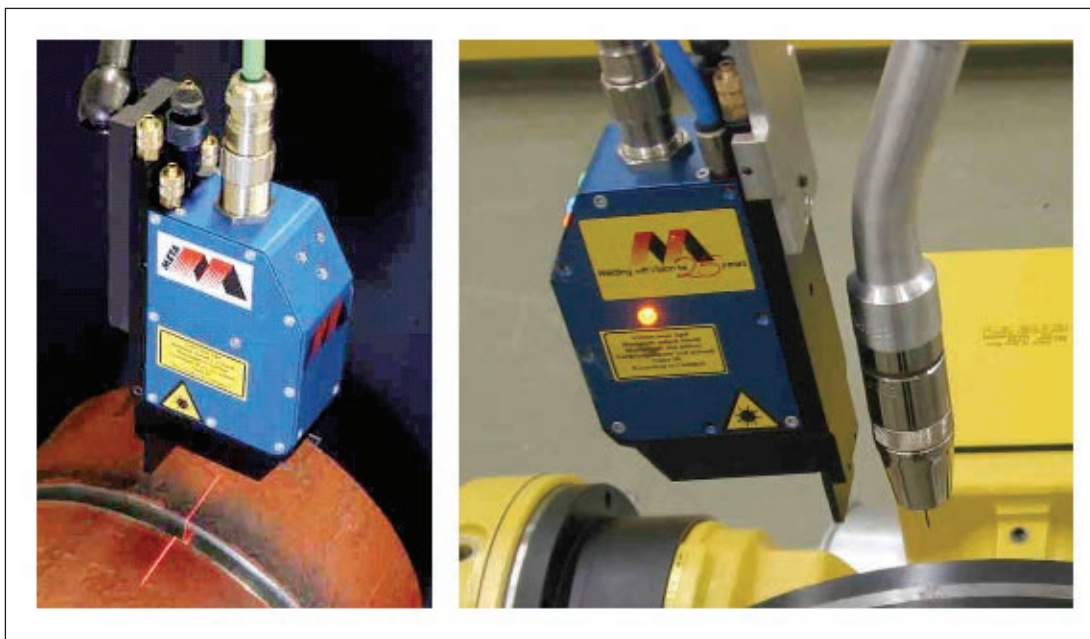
Лазерная камера METASLS-050 для слежения за осью шва, регулировки параметров сварки и возможности ее применения
